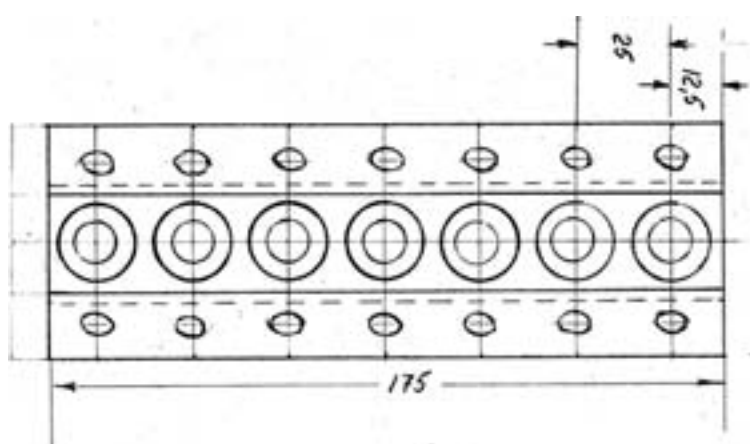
Корпус устройства для освещения с 7-ю парами светодиодов
